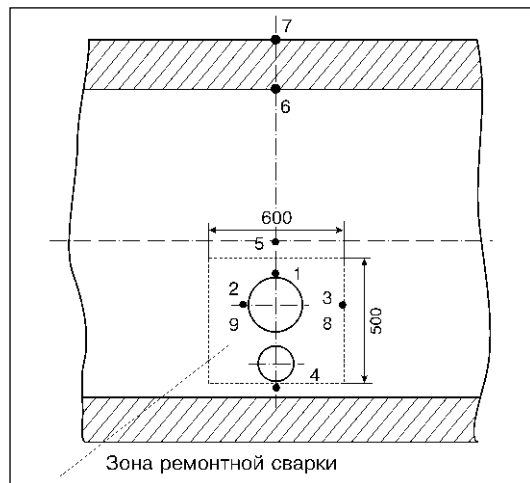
Схема размещения термопар на барабане ТЭЦ–ЗИЛ: 1 — лазер барабана; 2 — днище; 3 — сварной шов; 4 — обечайка; I–VIII — термопары
